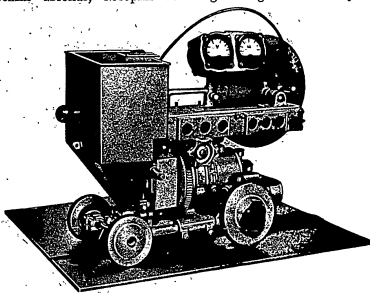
Сварочный трактор TC-17-M, настроенный на сварку стыковых швов без коппра
